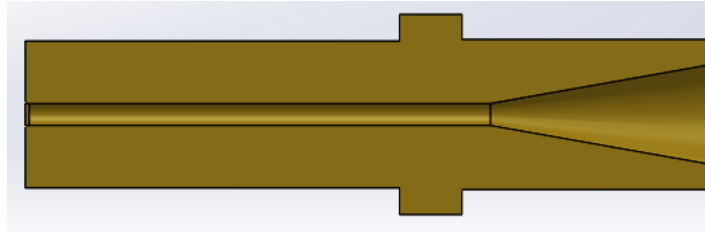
Diseño final boquilla de extrusión. Fuente: Propia.
